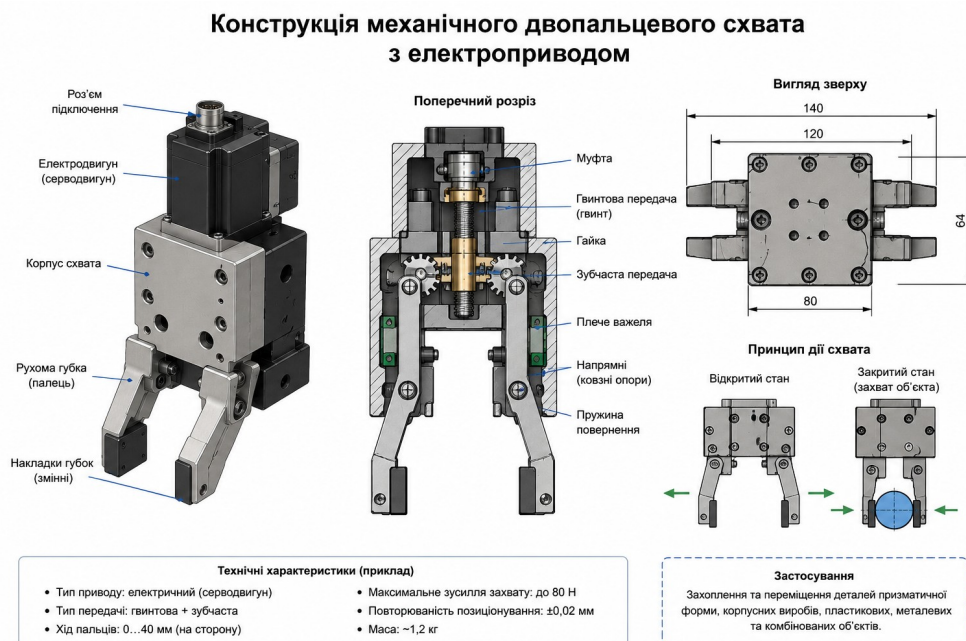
Конструкція механічного двопальцевого схвата з електроприводом
